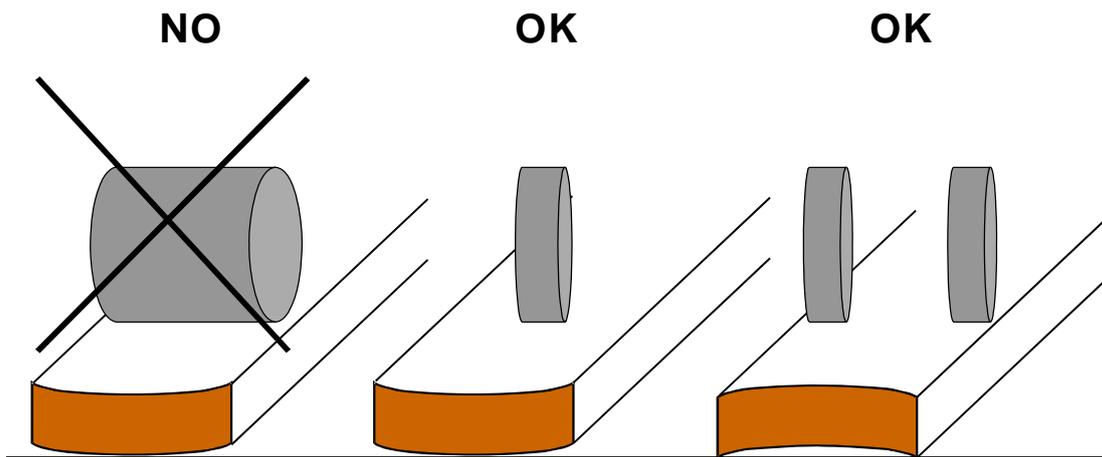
Rouleaux d'avancement recommandés pour éviter la fissuration des planches.
